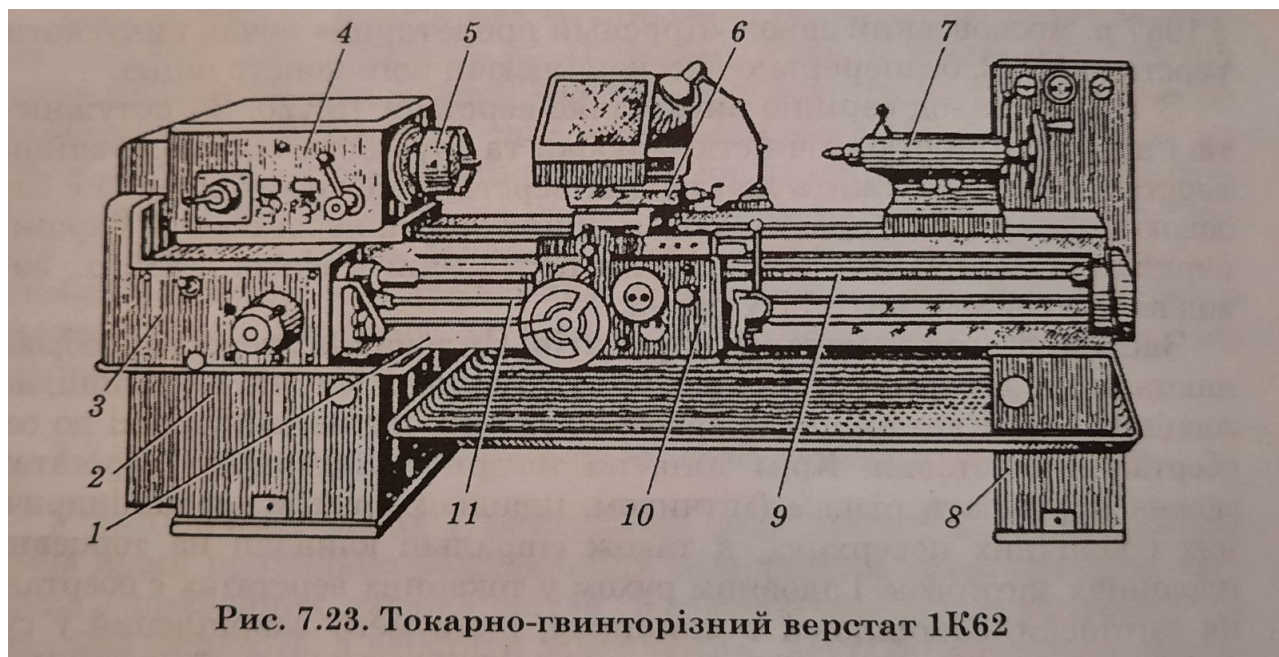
Токарно-гвинторізний верстат 1K62
